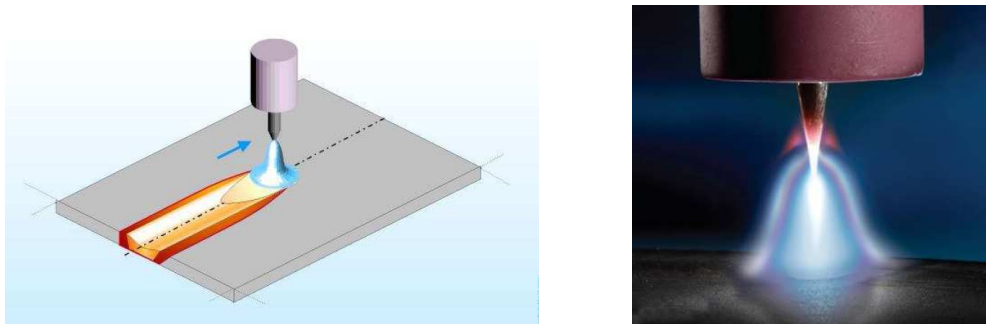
Soudage Tungsten Inert Gas ©EWM AG [16].
